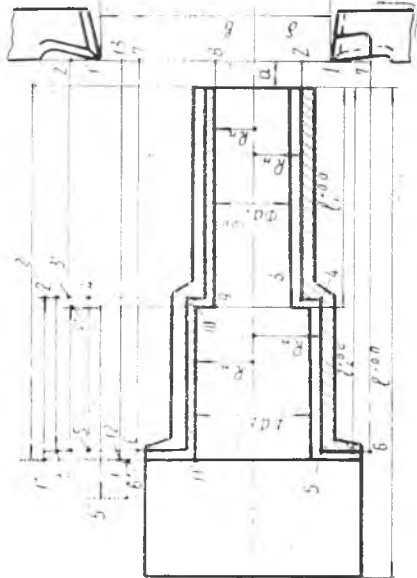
Схема обточки цилиндрических и торцевых поверхностей ступенчатого валика и путь движения резцов и упора.
